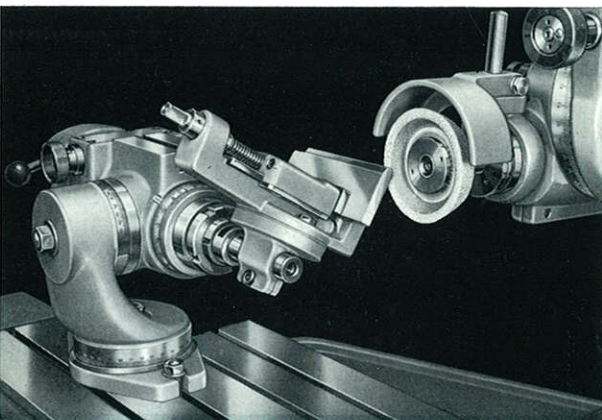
Schleifen einer Schrägfläche an Werkstück mit Maschinenschraubstock und HTR
